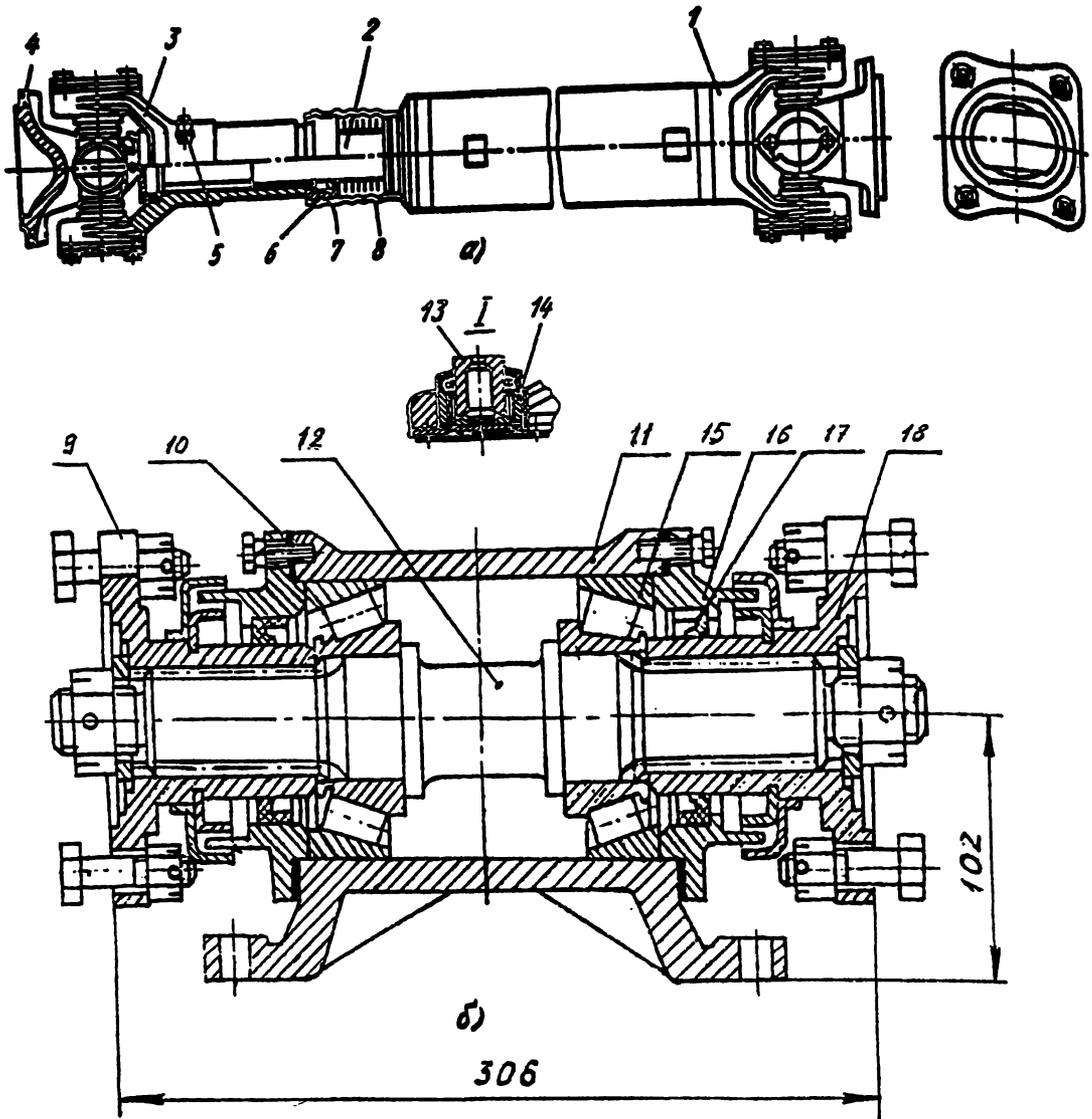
Карданный вал и промежуточная опора: а – вал; б – опора
